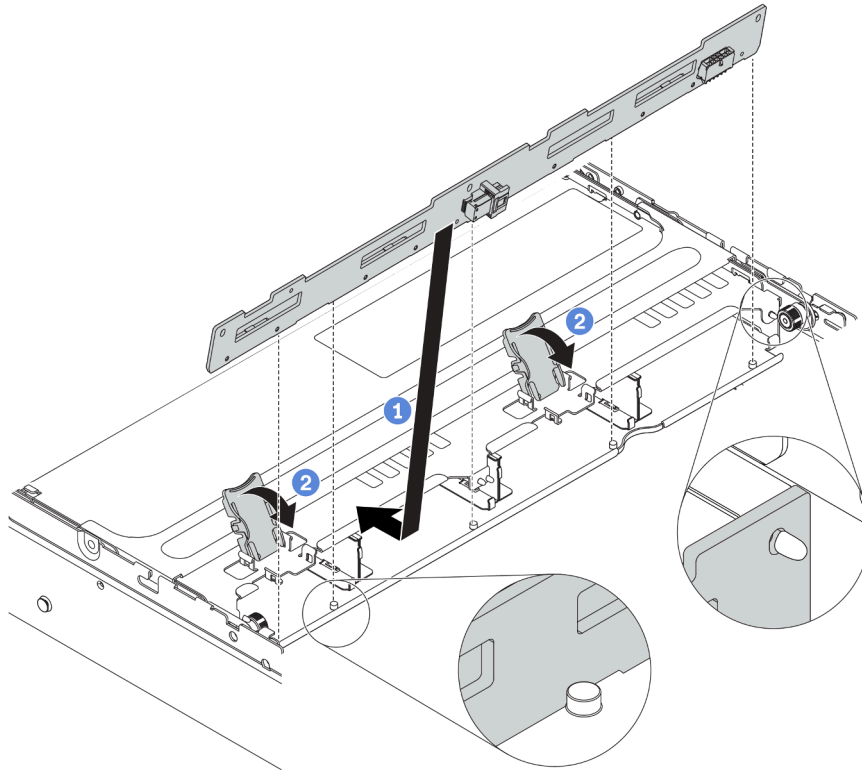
Installation du fond de panier d'unité 3,5 pouces central ou arrière
